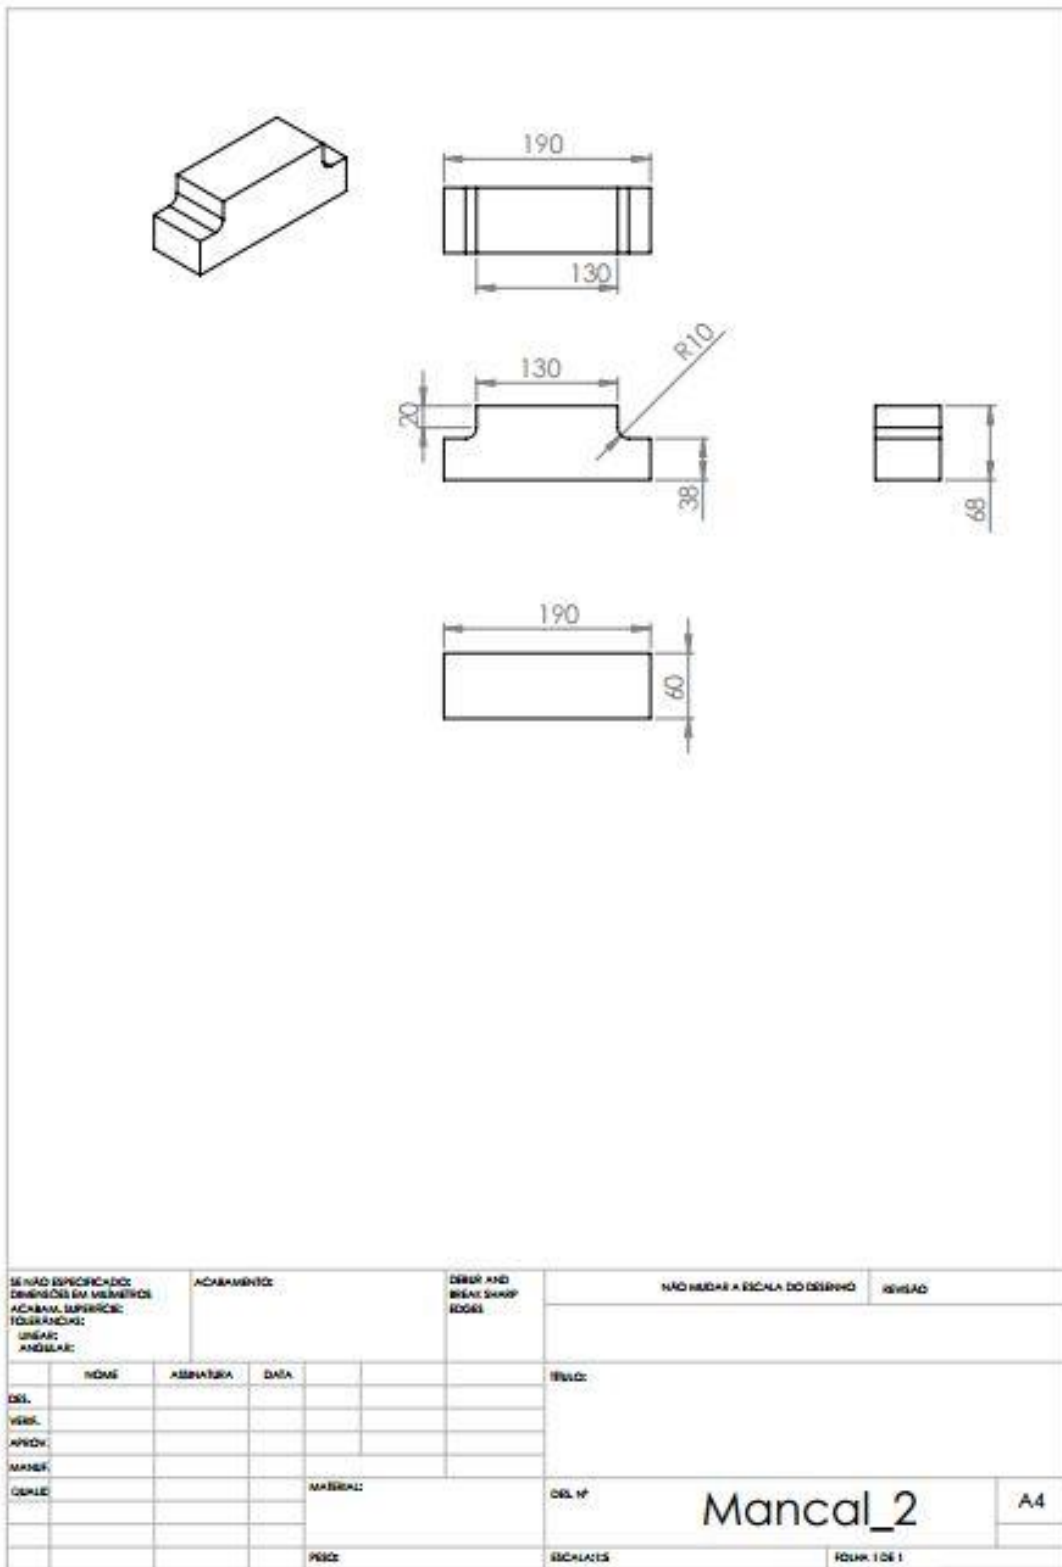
Desenho técnico do suporte do motor no eixo de saída.
